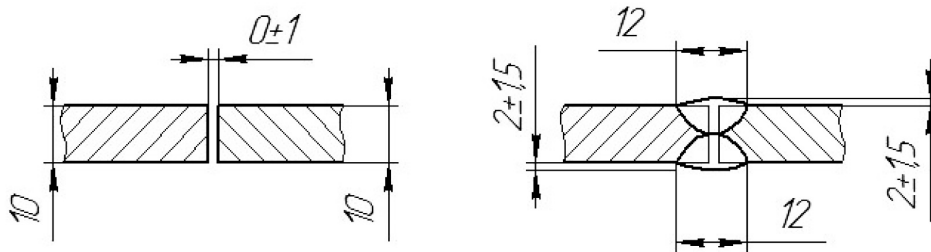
Поперечний переріз зварного з'єднання С7 за ГОСТ 14771-76
